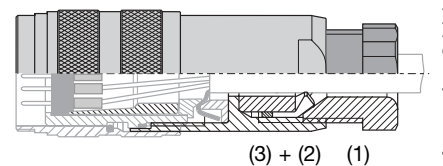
PG-Verschraubung montiert, Steckverbinder komplett
